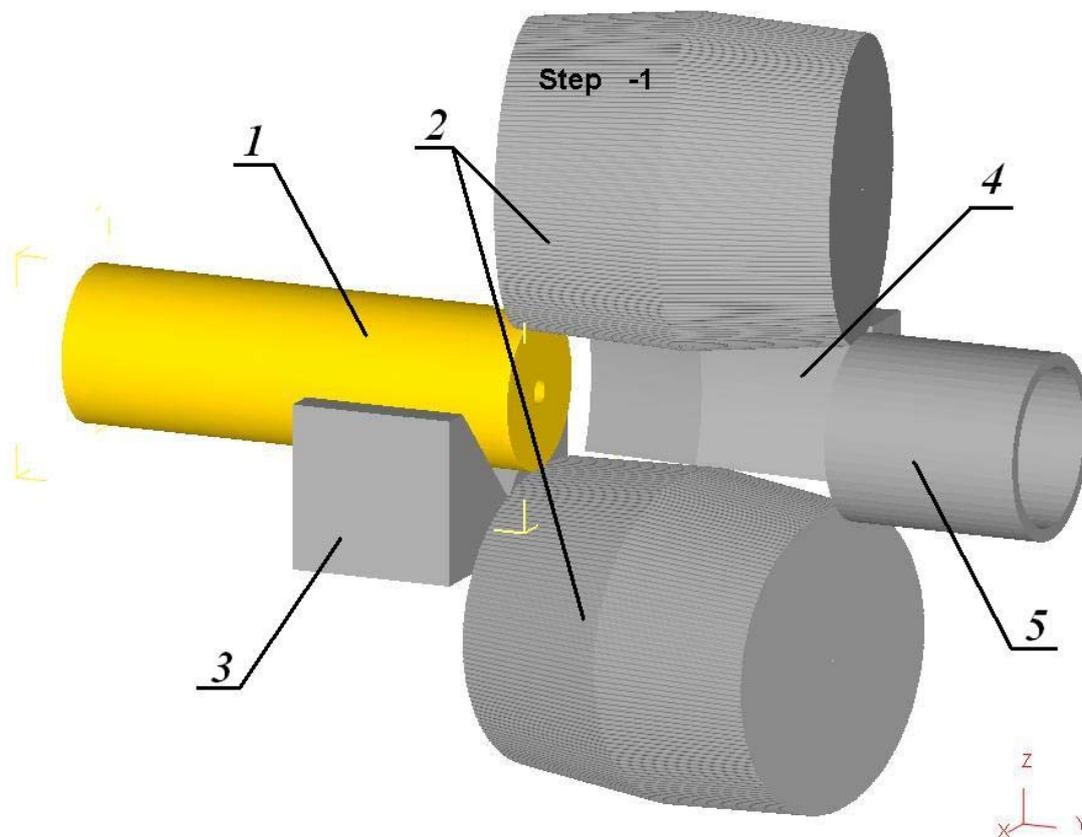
Очаг деформации двухвалкового стана винтовой прокатки: 1-заготовка; 2-рабочие валки; 3-удерживающий желоб; 4-направляющие линейки; 5-выходное кольцо.
